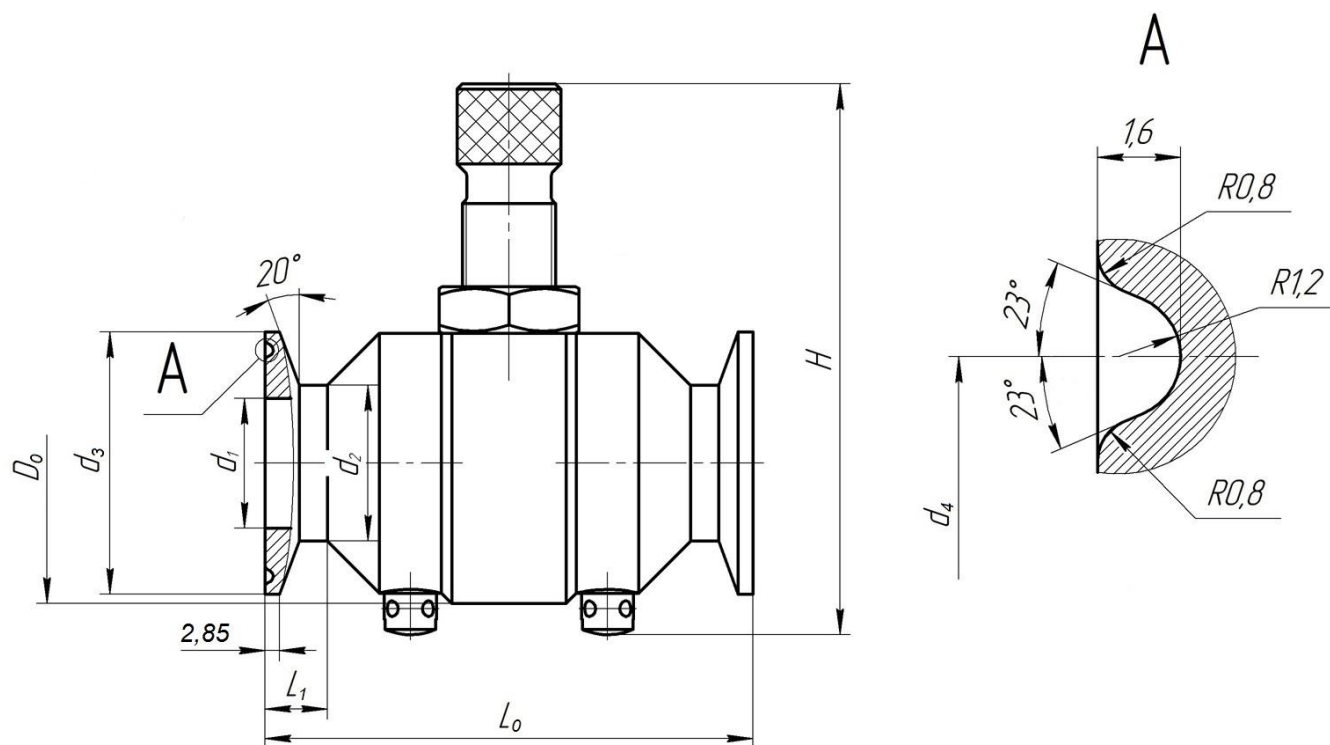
Габаритно-присоединительные размеры ПИП обозначения Z
